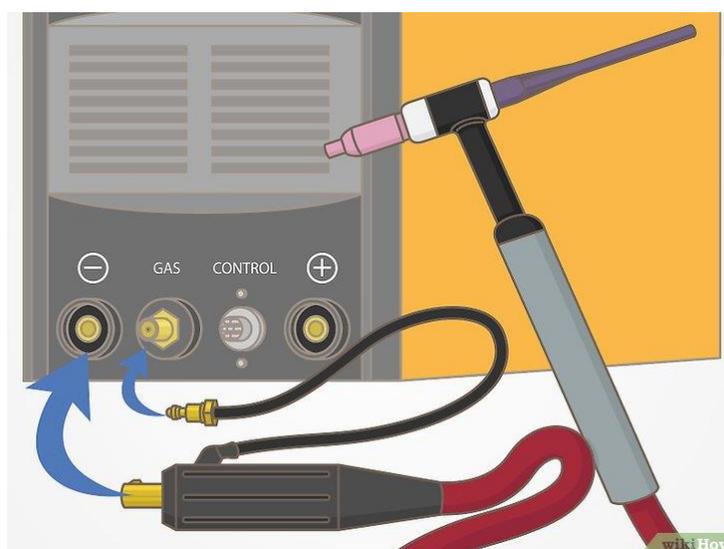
Conexiones GTAW (Fuente: wikihow.com)
